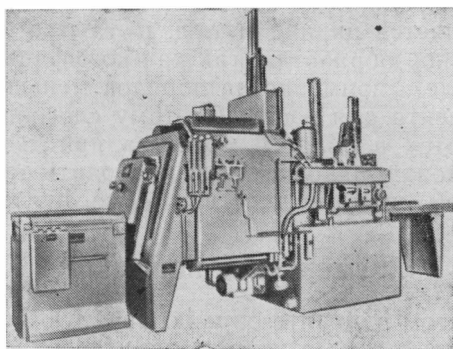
Общий вид универсальной установки для термической обработки, используемой для газовой цементации и карбонитрирования (заводское фото «Ипсен»)
